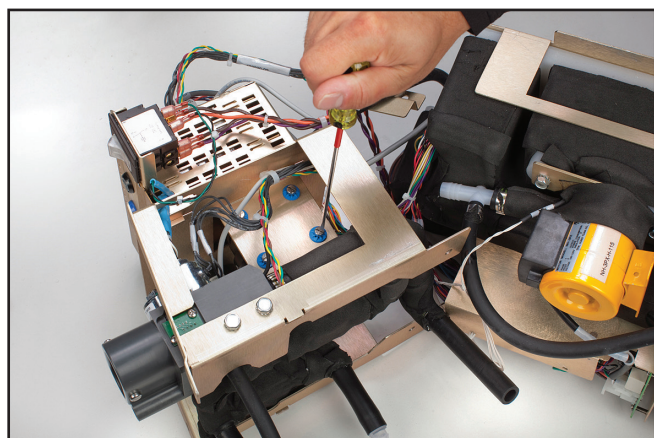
Desserrer les quatre vis entourées de bleu (étape 3)
